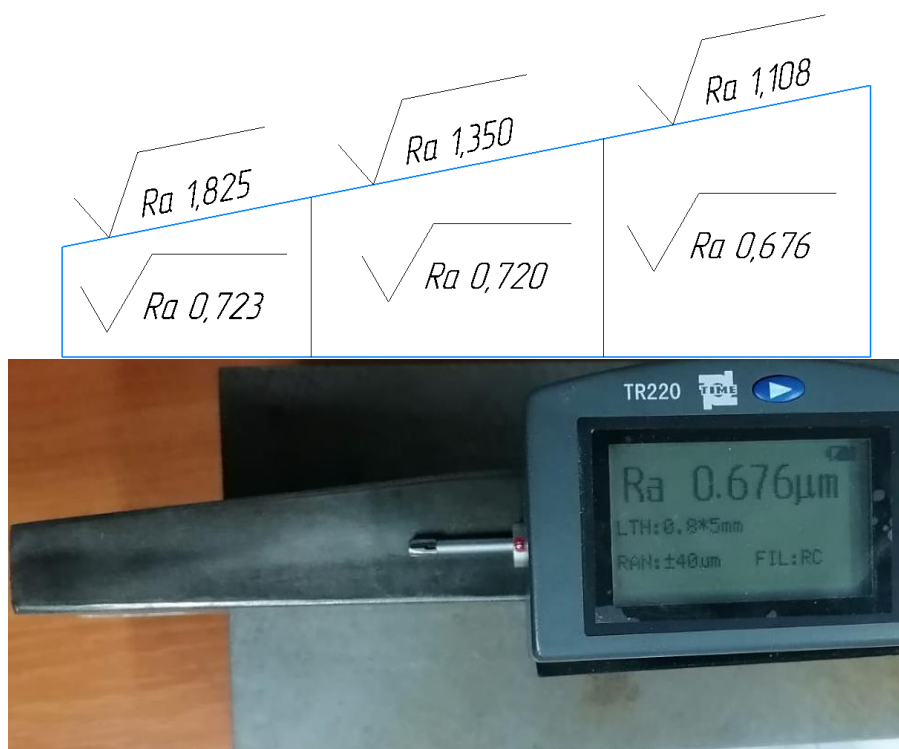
Измерение параметра шероховатости после обработки на рабочей поверхности изделия из материала Сталь 45
